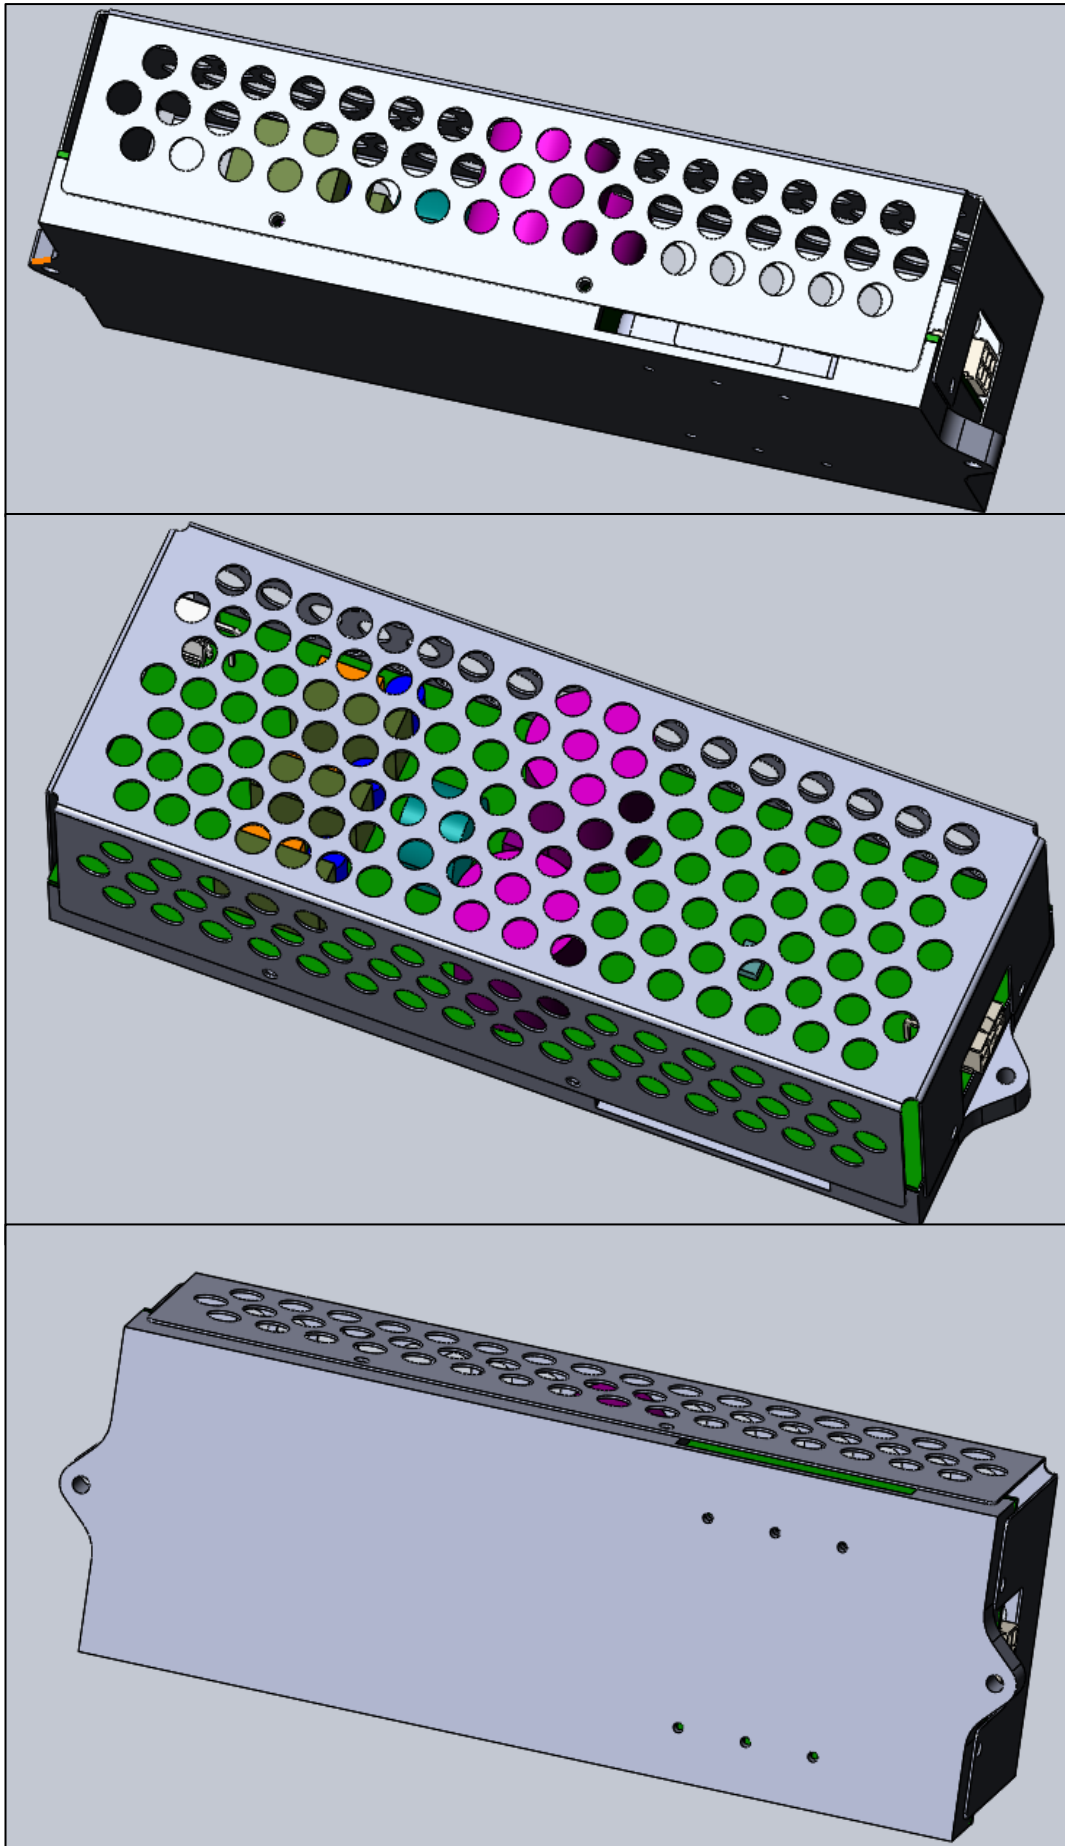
Внешний вид корпус прибора (с крышкой)
